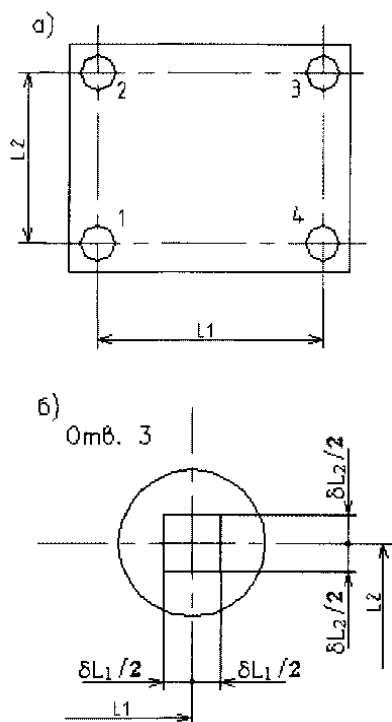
Простановка размеров при двухрядовом свинчивании деталей:
